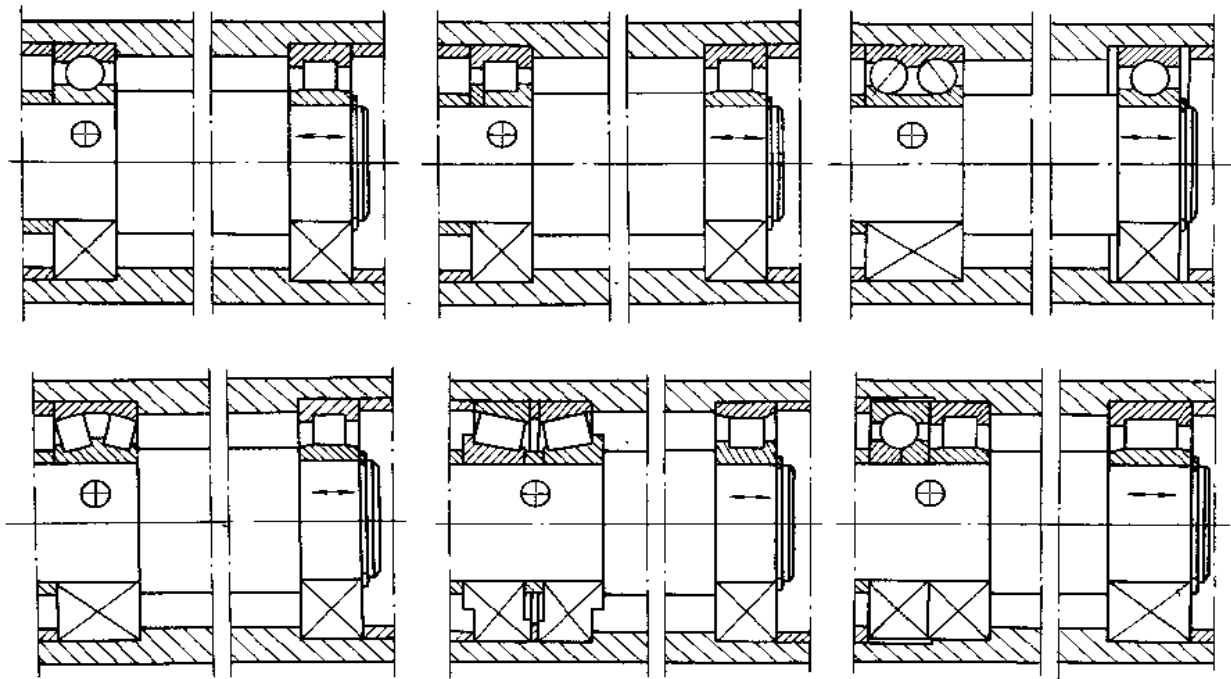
轴向定位轴承-轴向游动轴承配置 (⊕固定端, ↔游动端)
